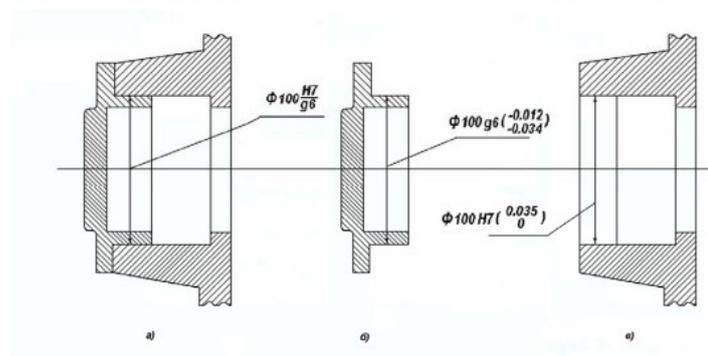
Обозначение посадки крышки в корпус (а) и полей допусков с отклонениями соединяемых поверхностей крышки (б) и отверстия в корпусе (в)
